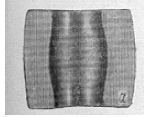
Формоміна тонкостінної кінцевої заготовки
